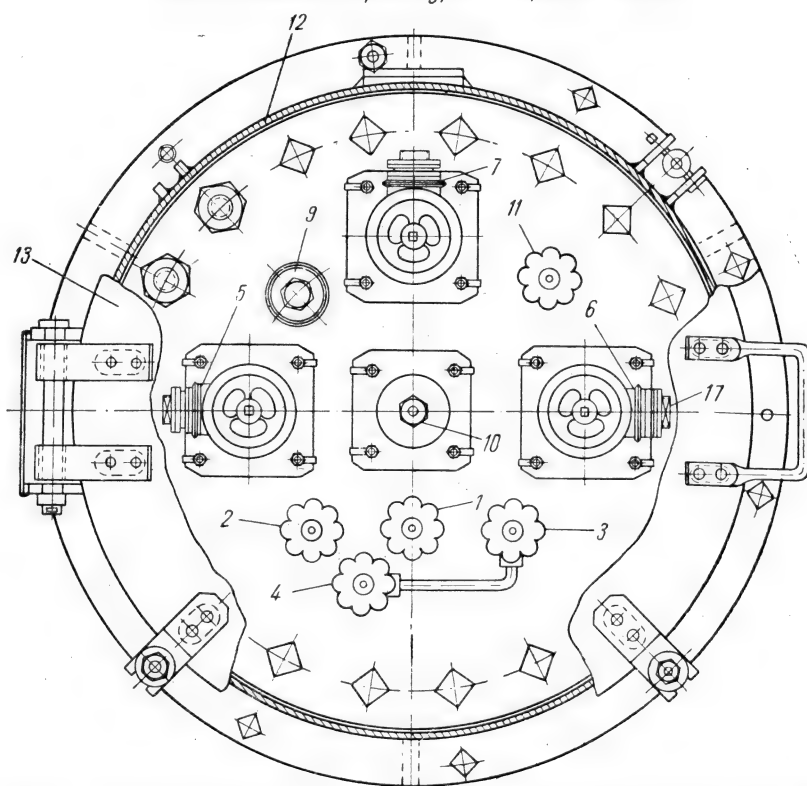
Схема расположения арматуры наверху железнодорожной цистерны для пропана:
